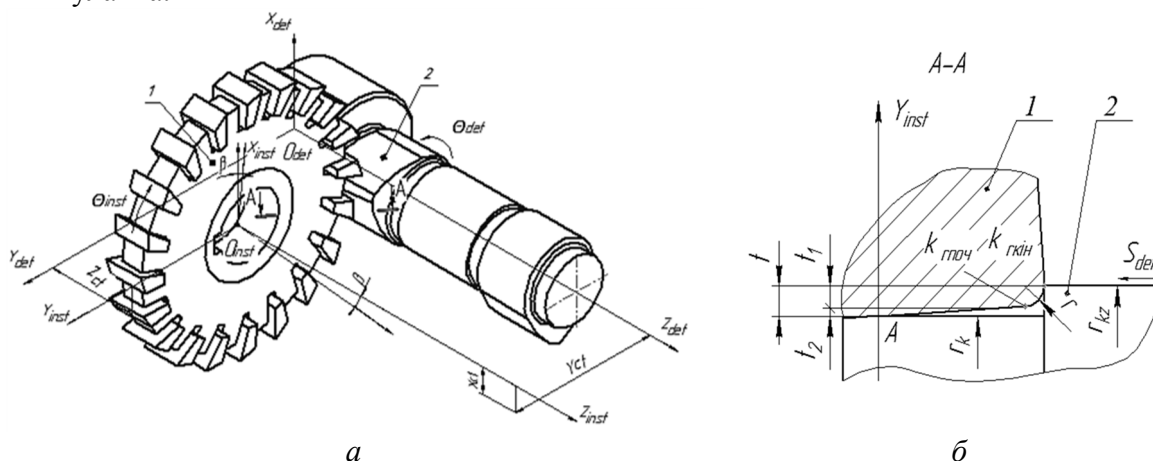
Схема фрезерування кулачка розподільного вала зі схрещеними осями інструмента та деталі: 1 – фреза; 2 – розподільний вал
